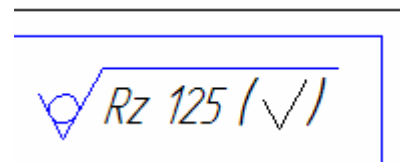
Примеры обозначения шероховатости на чертеже:
